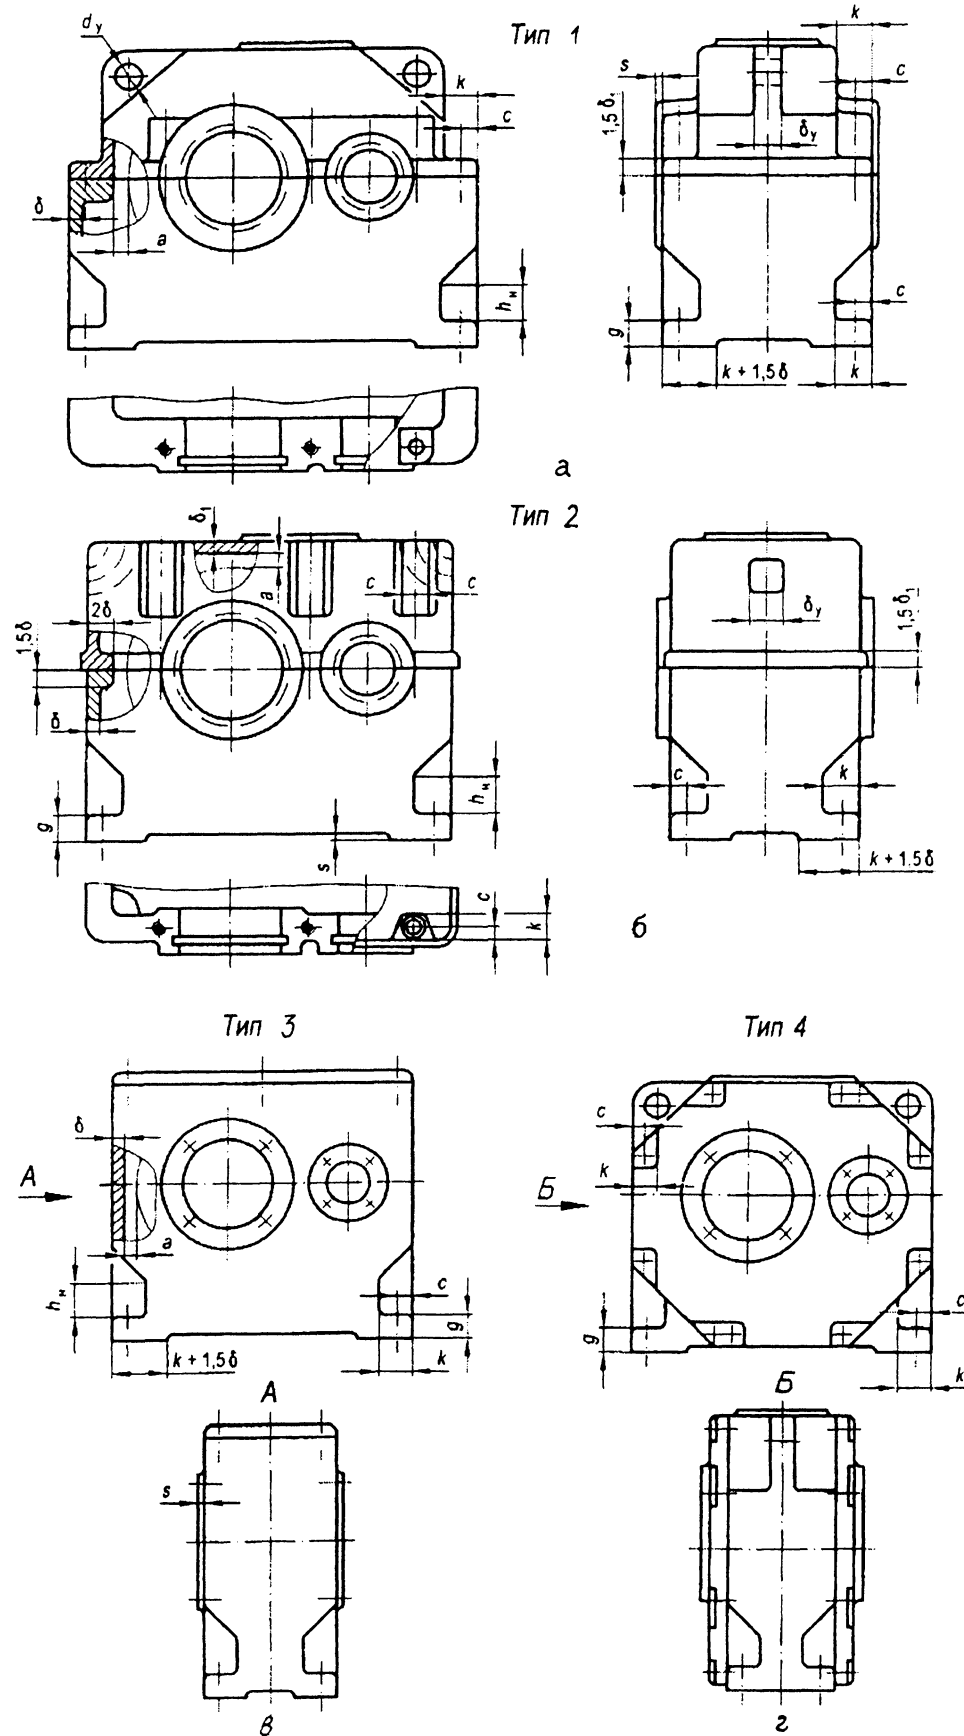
Основные типы конструкций корпусов редукторов [1]
